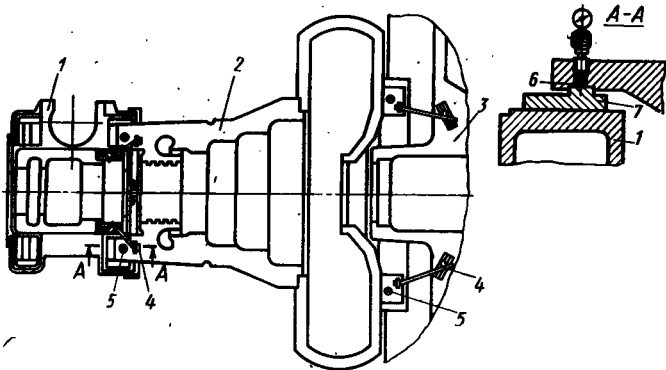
Схема расположения динамометров и индикаторов на цилиндре:
